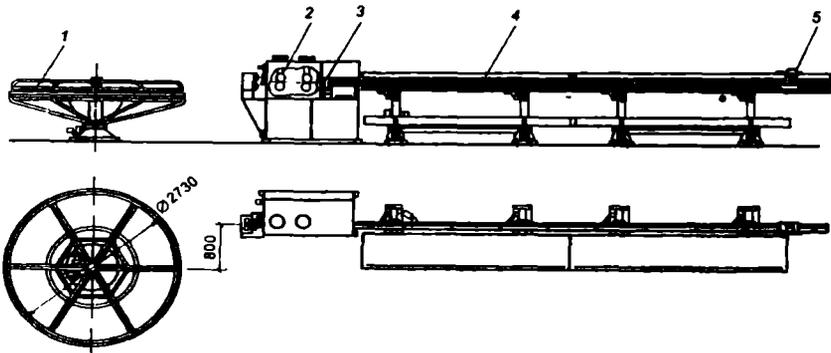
Установка СМЖ-123 для заготовки прутков мерной длины из канатов и высокопрочной проволоки:
